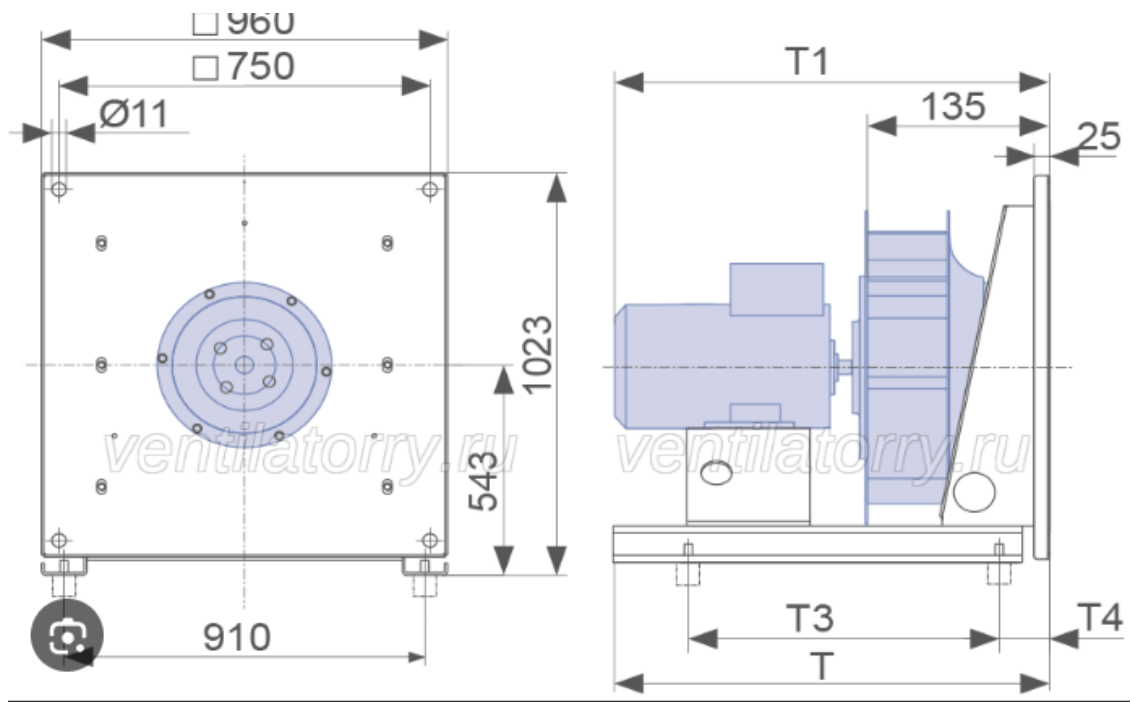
Креслення вентилятора ER71C-4DN.L7.1R
